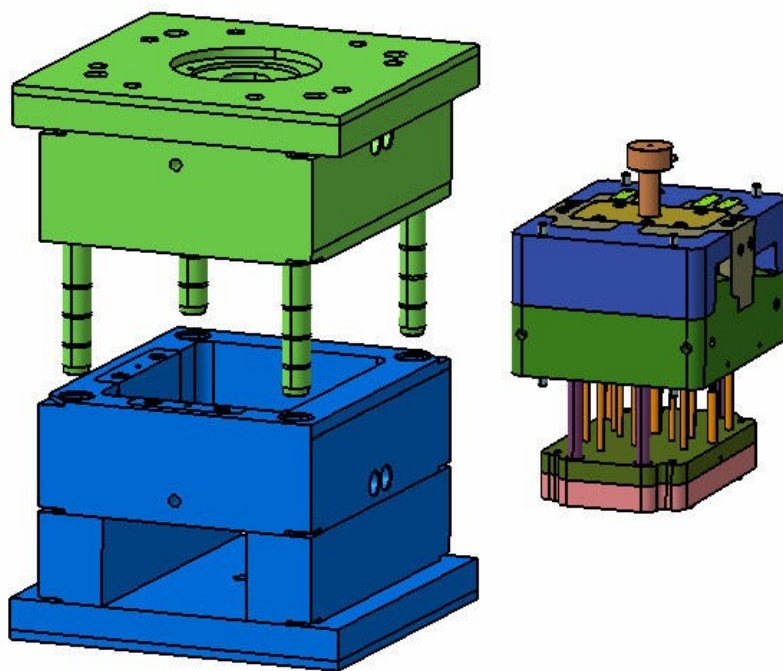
Vložkování formy pro jednodušší opracování
